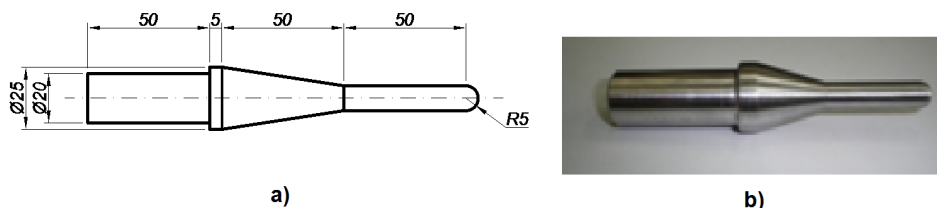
a) Desenho Projetivo da Ferramenta de Estampar, b) Ferramenta de Estampar
